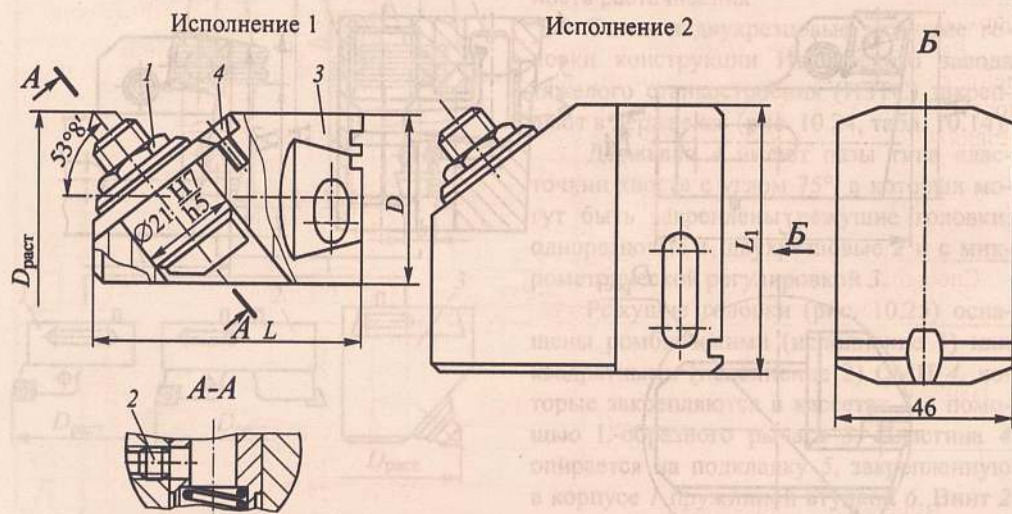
Режущая головка с микрометрической регулировкой резца
